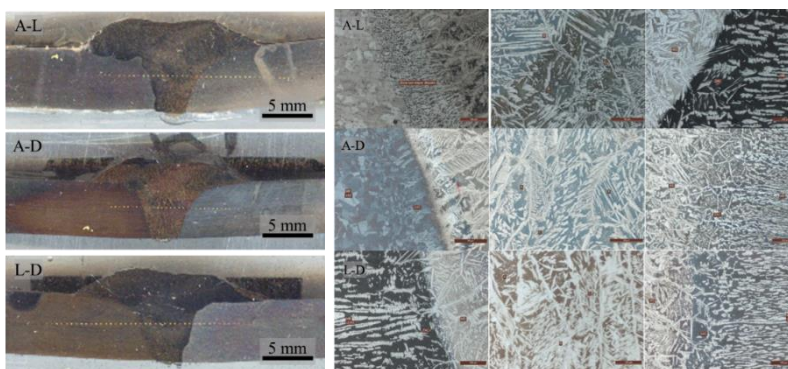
Macro y micrografías de las uniones soldadas, MB: Metal base, ZAC: Zona afectada por el calor, MS: Metal de soldadura.
